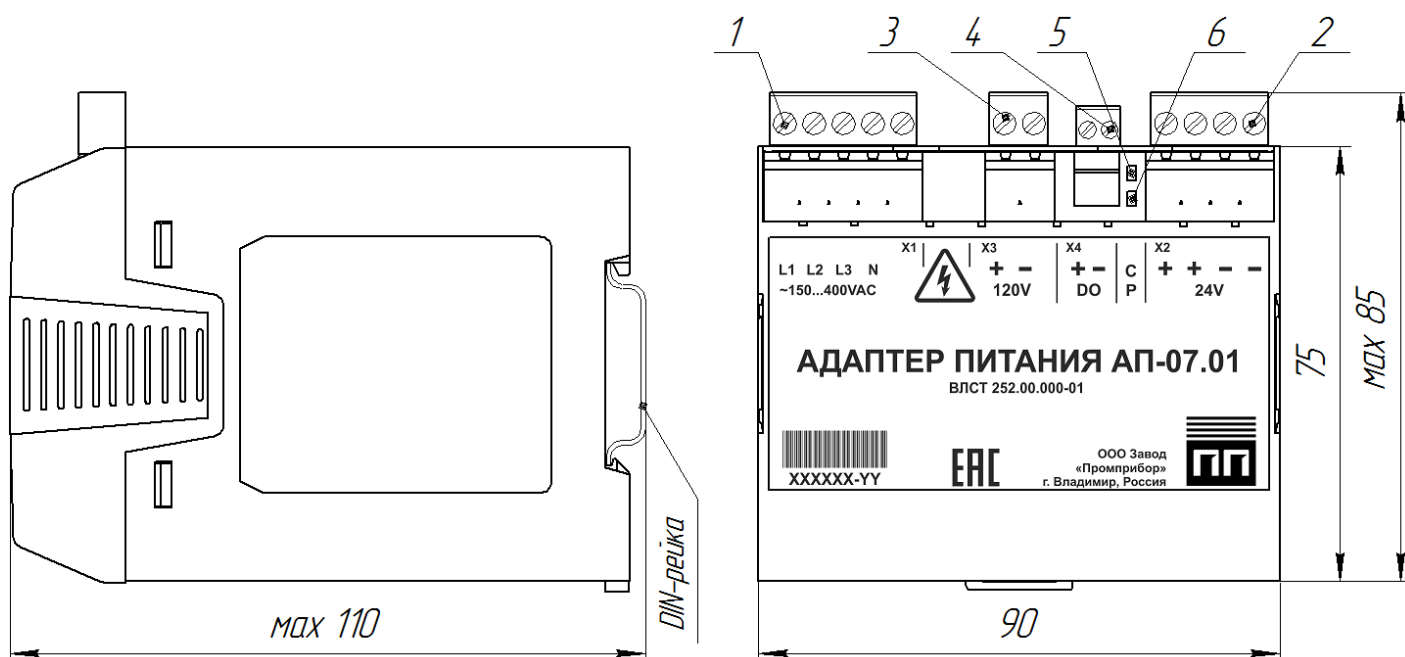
Внешний вид и размеры адаптера АП-07.01
